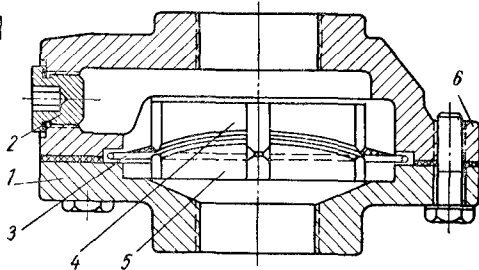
Вибратор: 1 — корпус; 2 — крышки; 3 — боек.
